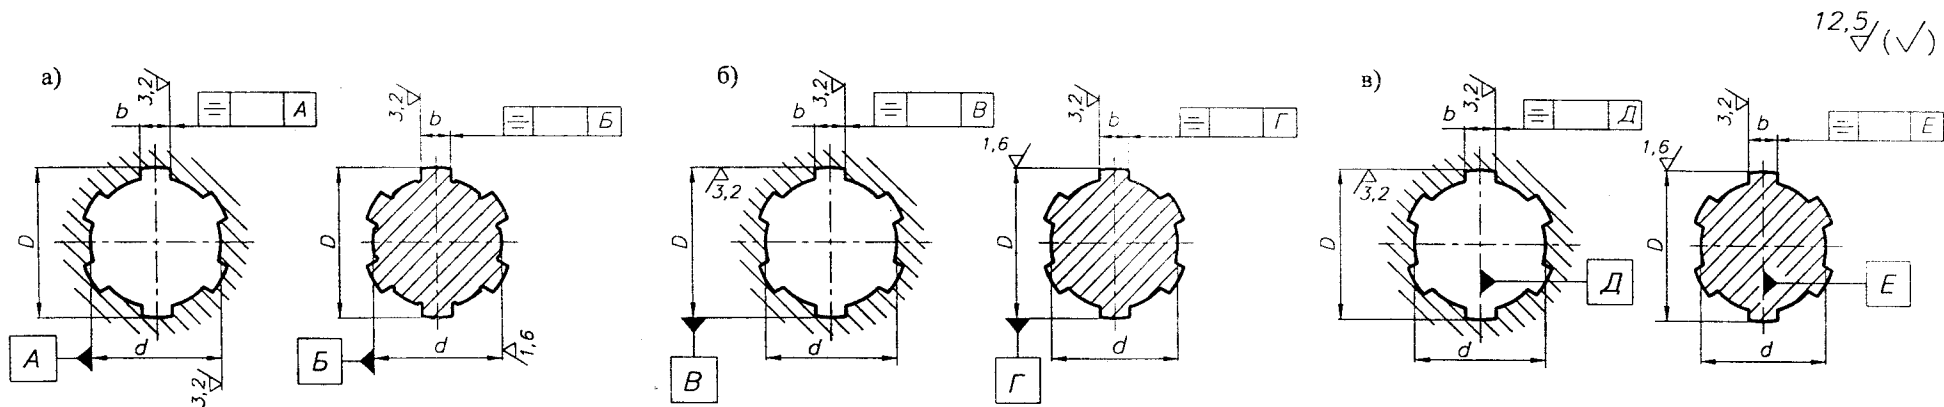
Базовые поверхности, шероховатость, допуски формы и расположения поверхностей шлицевого прямобочного соединения при центрировании: а) по d ; б) по D ; в) по b
